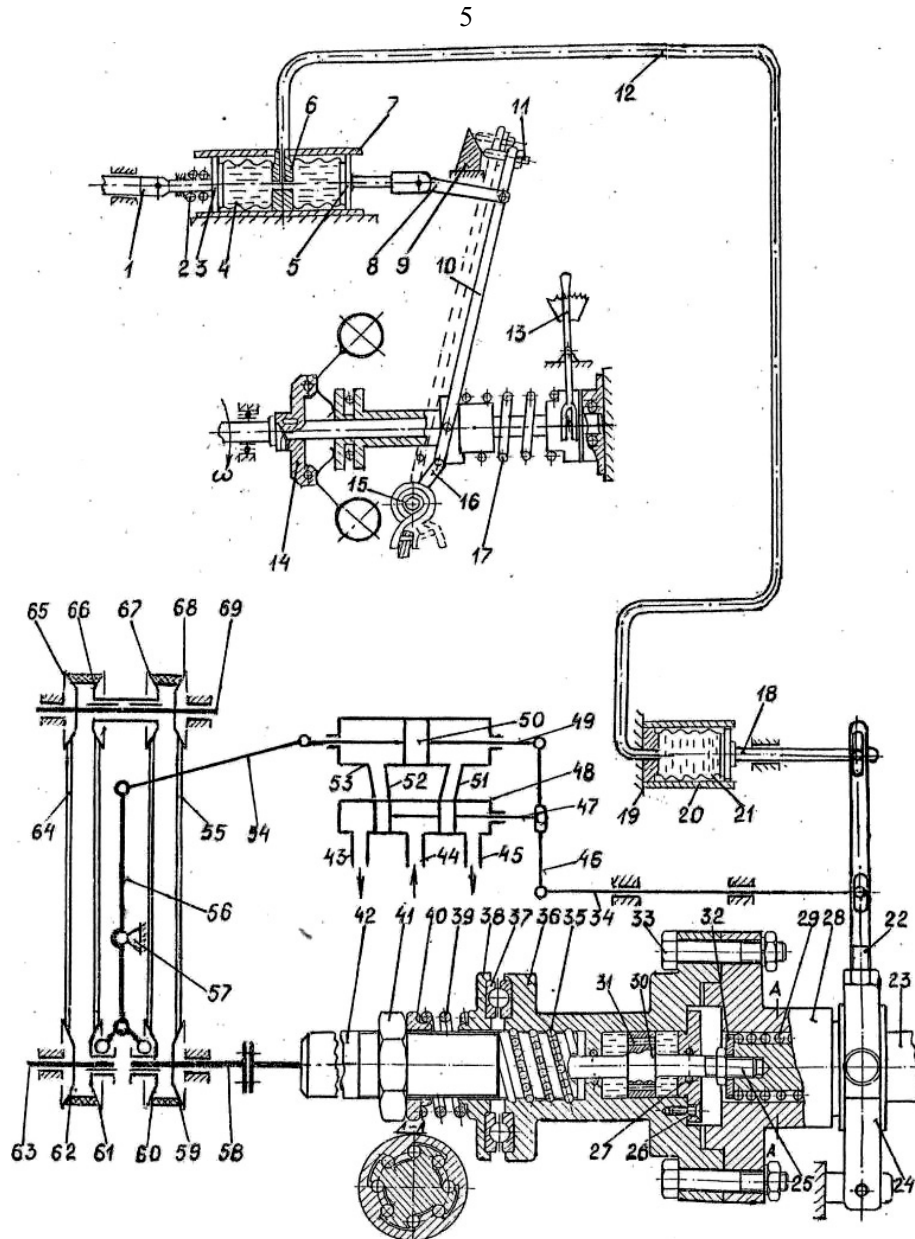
Конструктивна схема САРЧ обертання привода землерийної машини.
